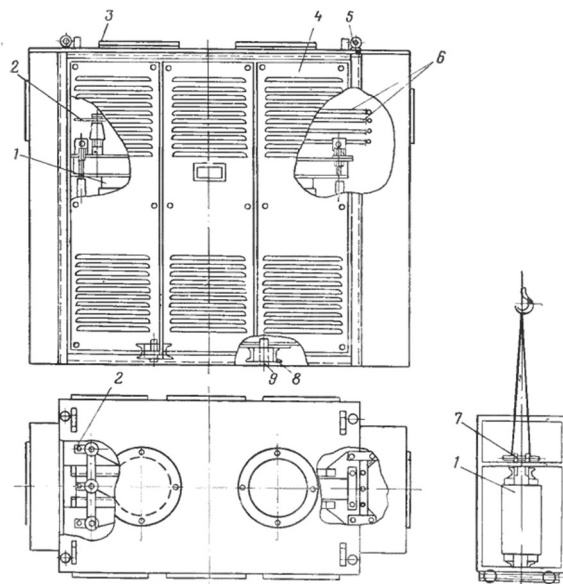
Силовой трансформатор (ТС): 1 — активная часть; 2 — ввод ВН; 3 — крышка люка; 4 — кожух; 5 — кольцо для подъема трансформатора; 6 — шины НН; 7 — планка для подъема активной части; 8 — тележка; 9 — каток.
